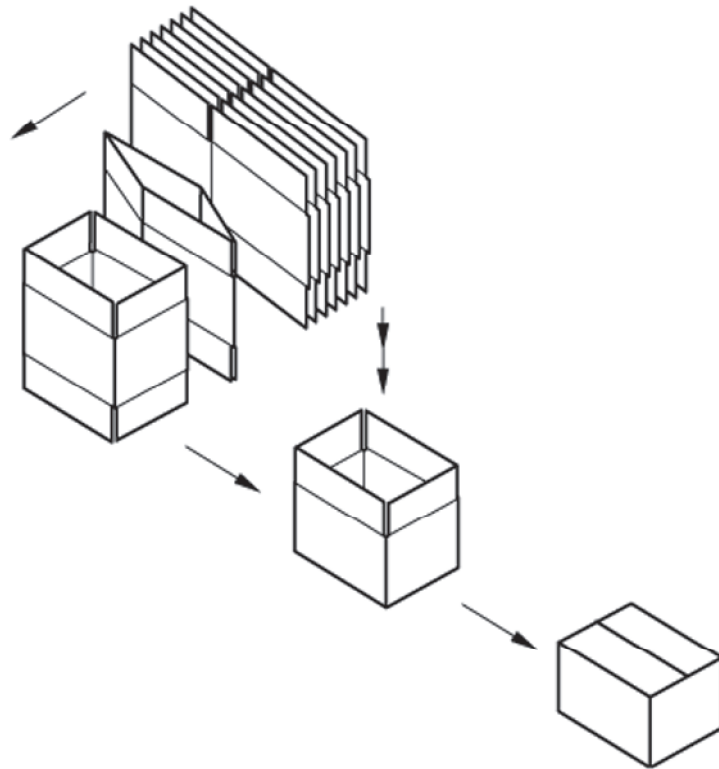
Faltschachtelverpackungsmaschine mit Zuführung von oben
